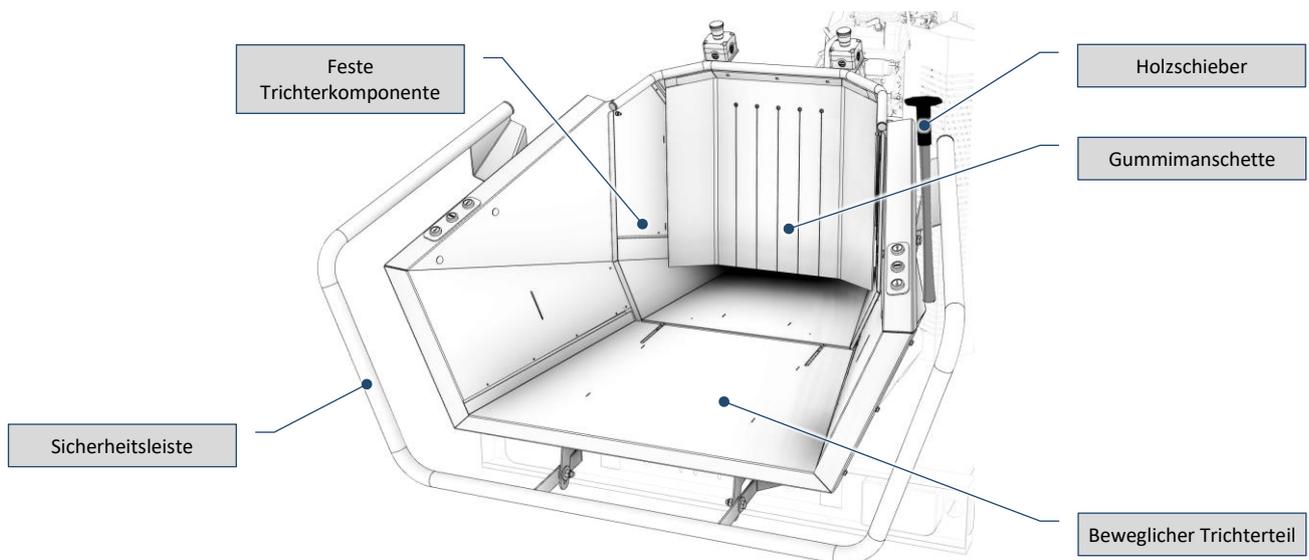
Einfülltrichter (Frontalansicht)
